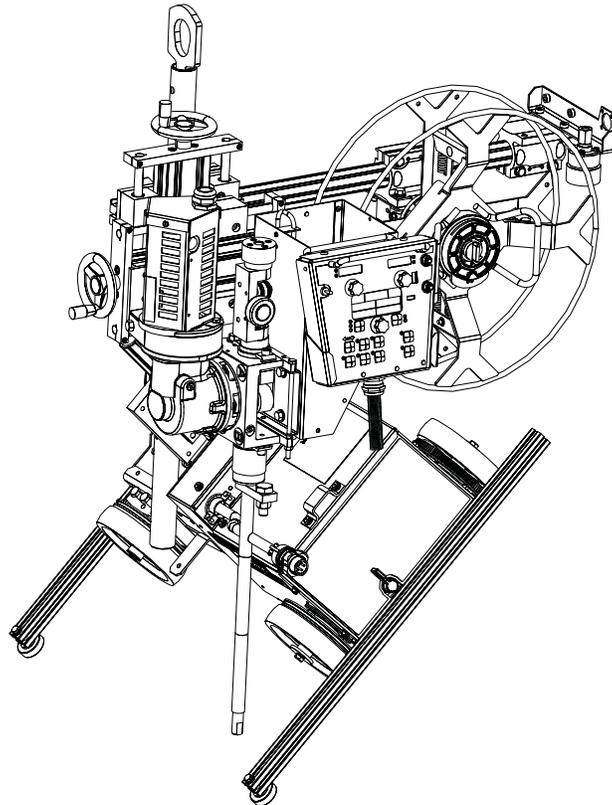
FILETE PLANO (ATRAVIESA) VISTA POSTERIOR
